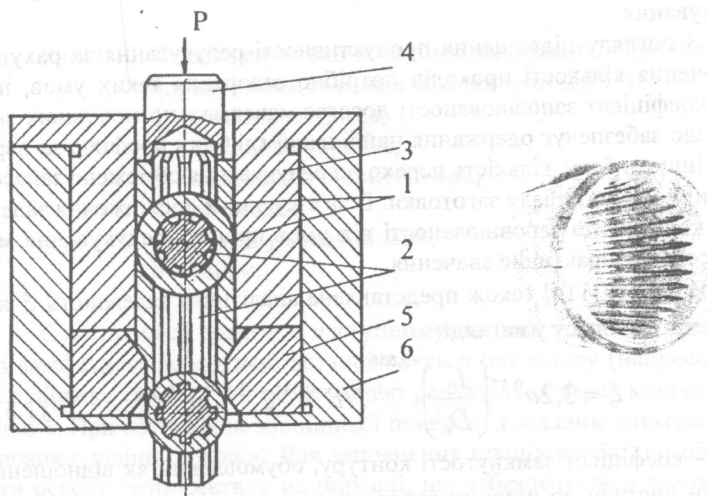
Схема формування внутрішніх шліців в трубній заготовці шліцьового з'єднання карданного вала дизель-потяга ДП-2
